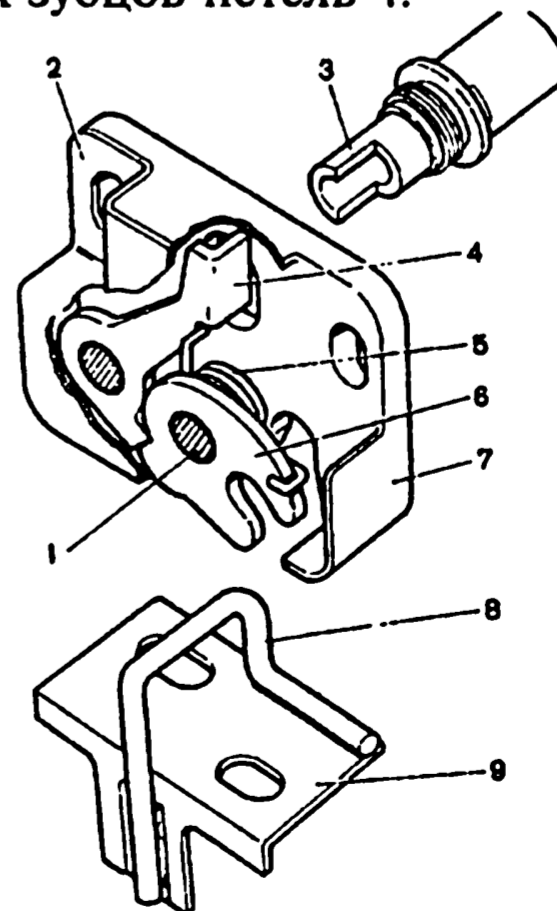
Замок багажника: 1 - ось ротора; 2 - крышка корпуса замка; 3 - удлинитель привода замка; 4 - рычаг; 5 - пружина; 6 - ротор; 7 - корпус замка; 8 - фиксатор; 9 - пластина фиксатора
